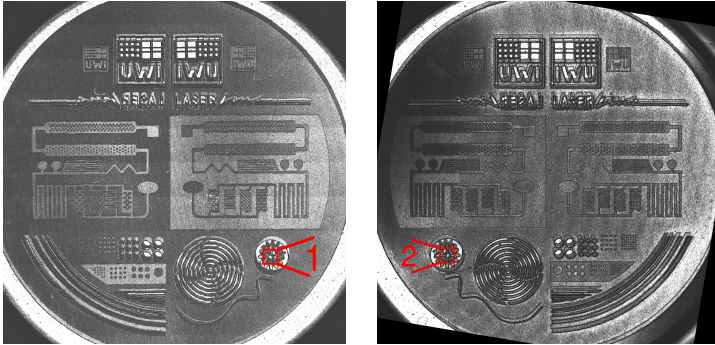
Intensitätsprofil des Werkzeugs einer Teststruktur (links) und einer mit Chrom beschichtete geprägte Probe (rechts);
